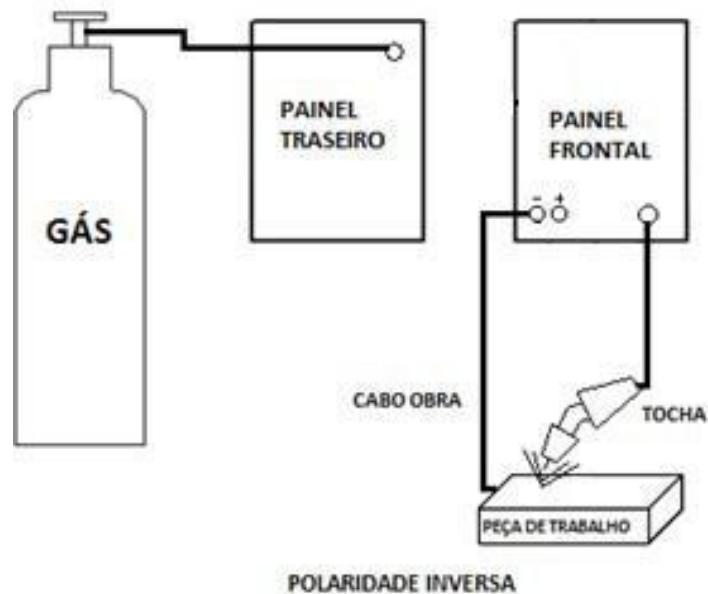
Diagrama conexão soldagem MIG/MAG.
